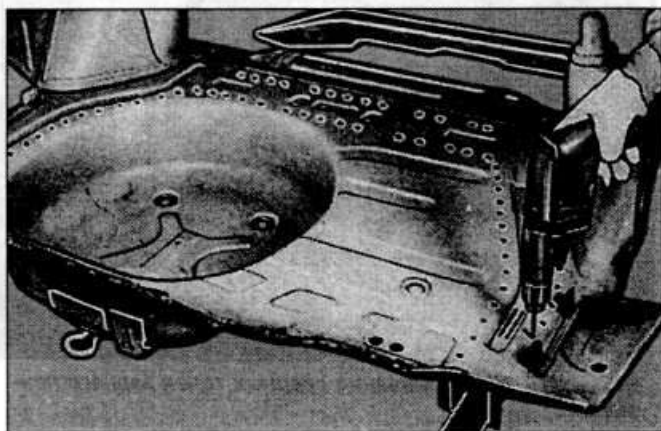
Высверливание точек сварки панели с лонжероном
